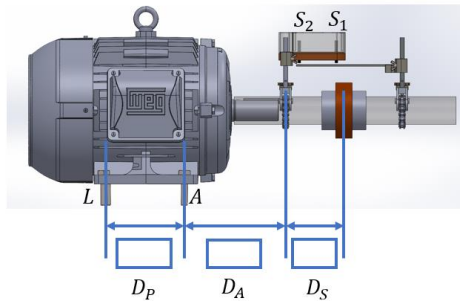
Montaje de prototipo. Fuente: Autores.
